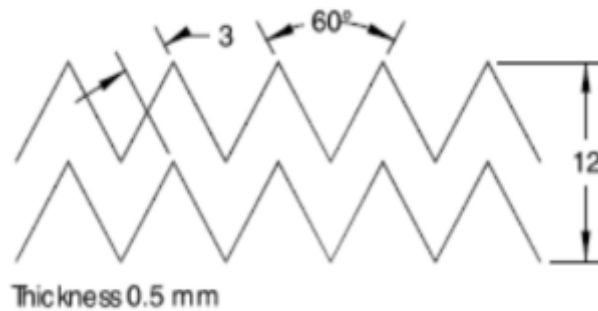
dimension du Modèle de rugosité sous forme de zigzag 60°[23]
